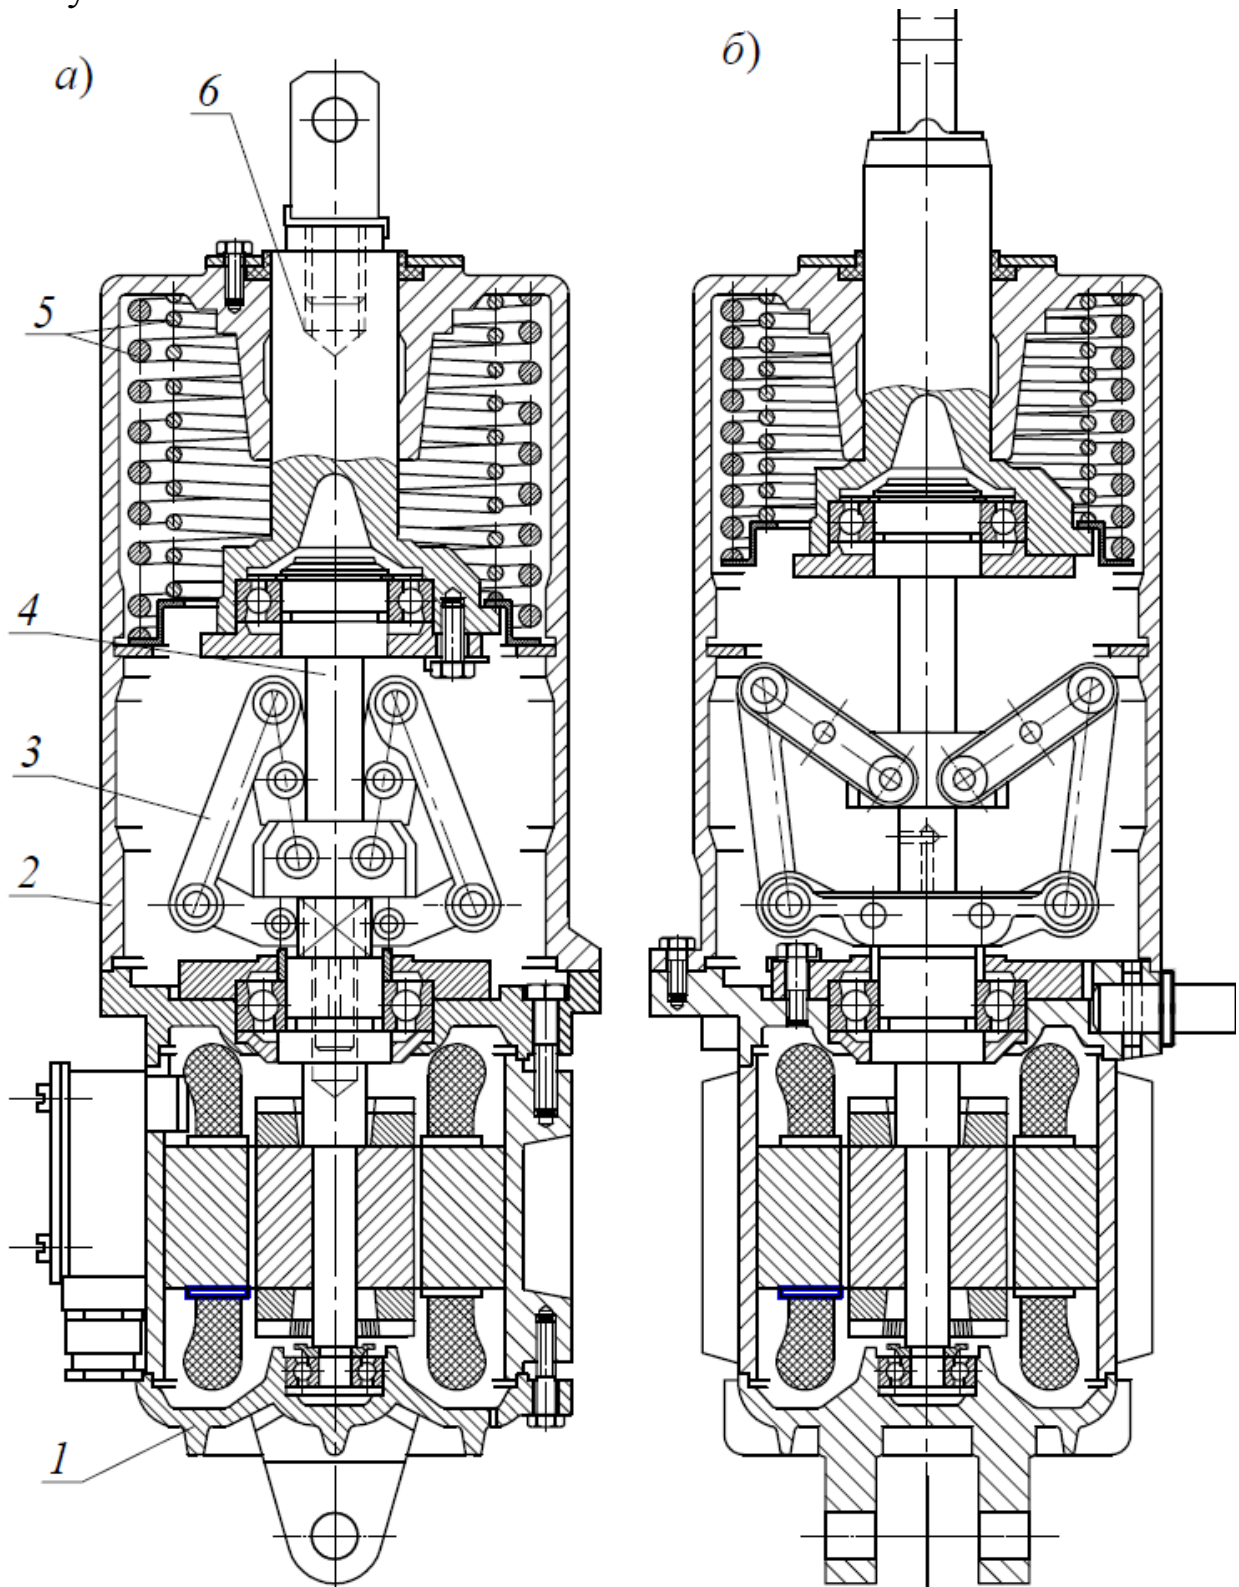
Центробежный толкатель: *а* – положение покоя; *б* – положение при включенном двигателе толкателя
